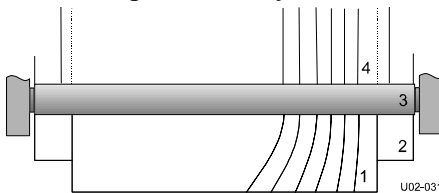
Rides dues à un défaut d'alignement du cylindre.
